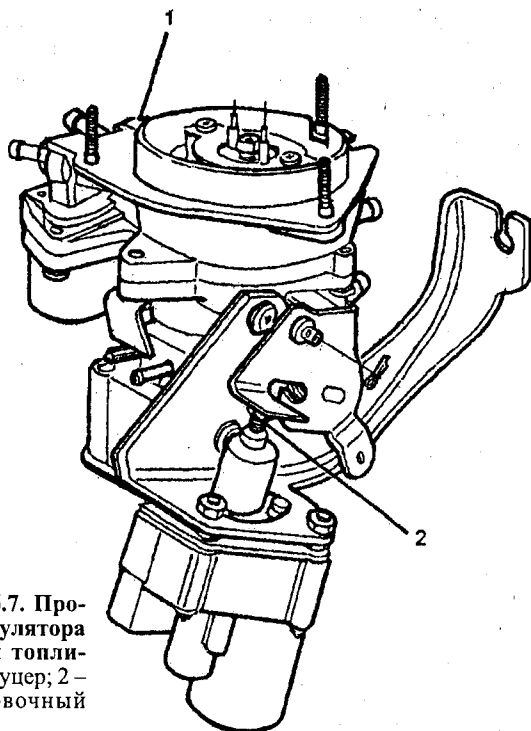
Проверка регулятора давления топлива: 1 – штуцер; 2 – регулировочный винт
